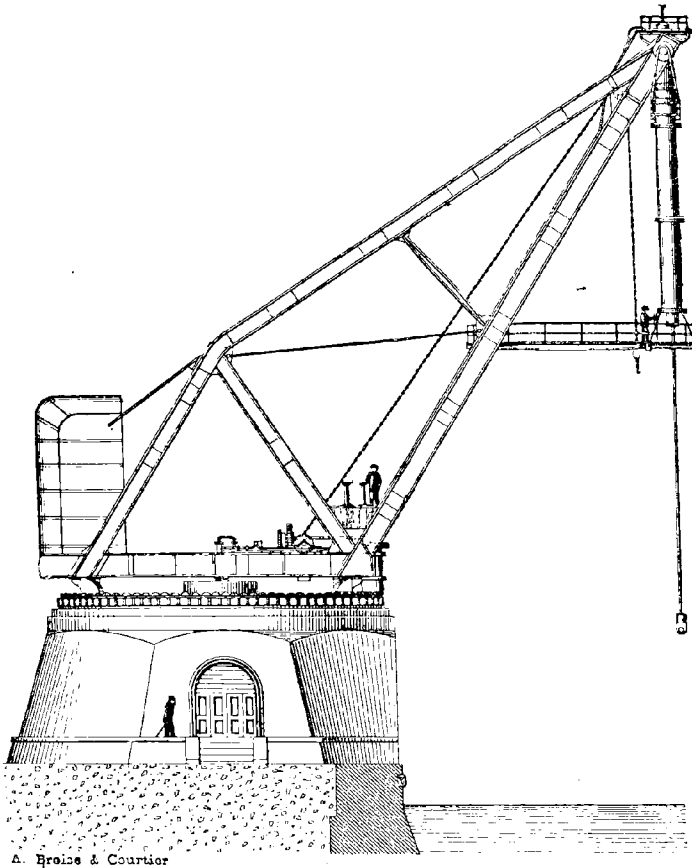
Grue hydraulique de 160 tonnes (élévation).
